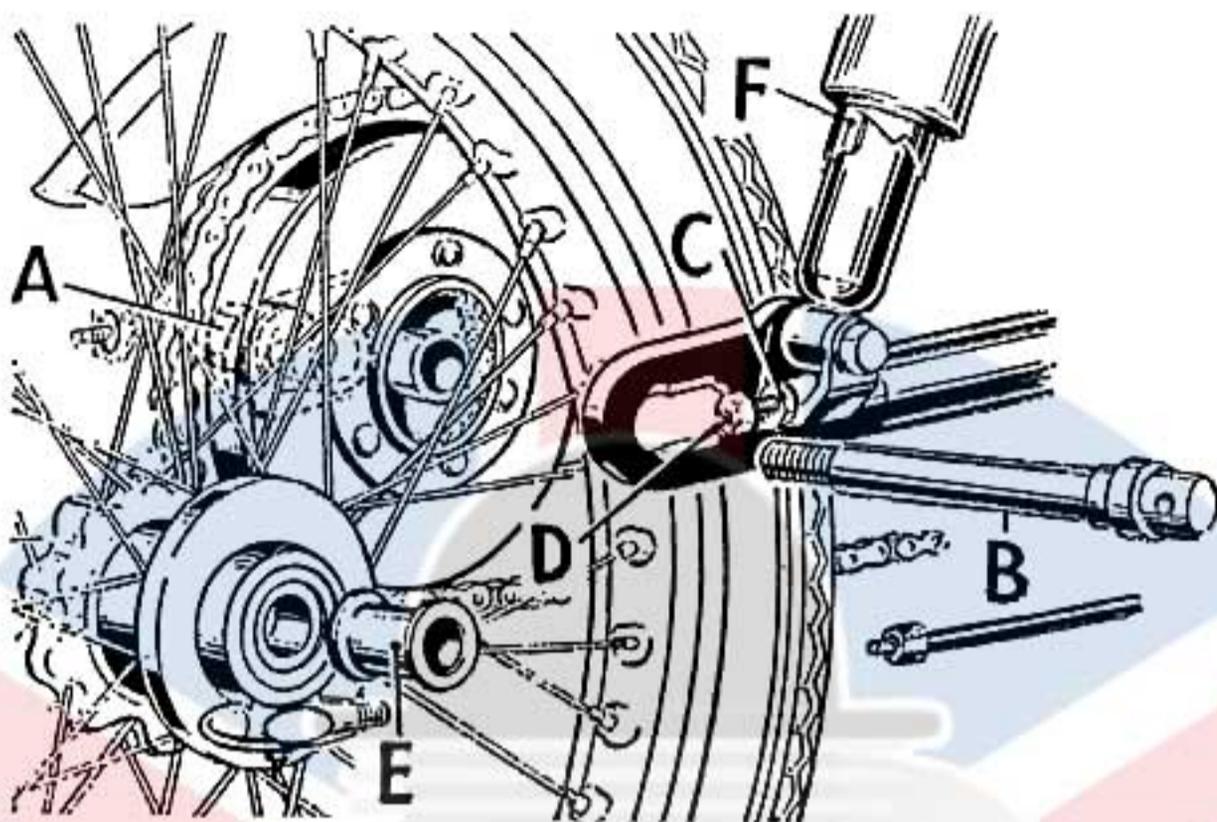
Retrait de la roue arrière, montrant aussi la position des boulons de réglage. Réglage de la chaîne sur les modèles A.
